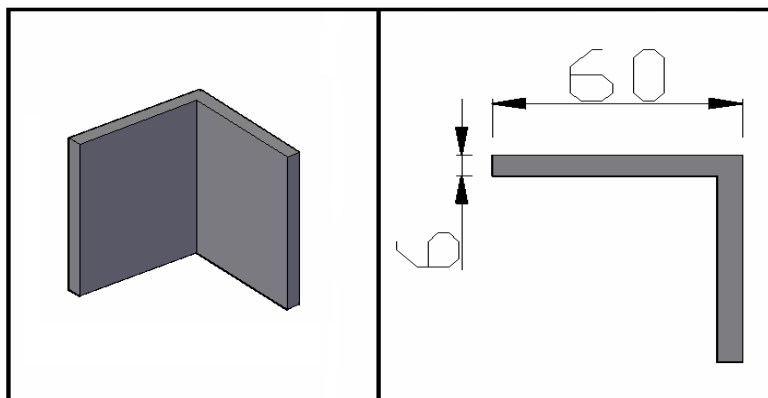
PERFIL PARA ESTRUCTURA DE MÁQUINA DE ENSAYOS.
